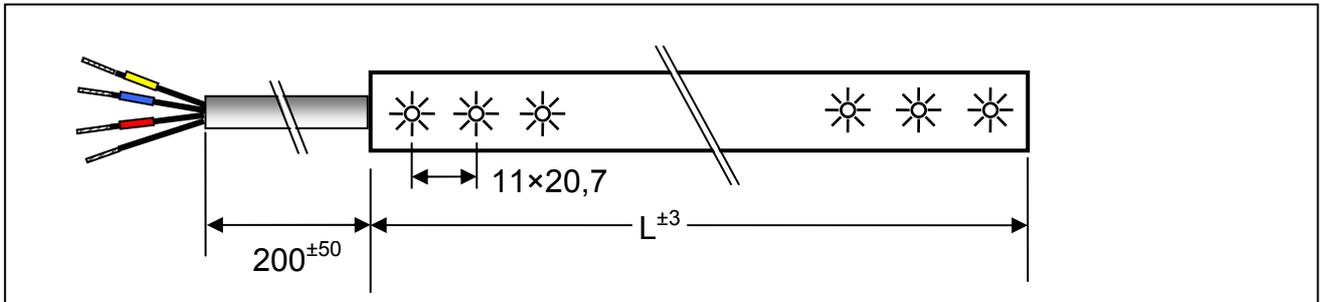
Einseitiger Anschluss (Gehäusevarianten)
